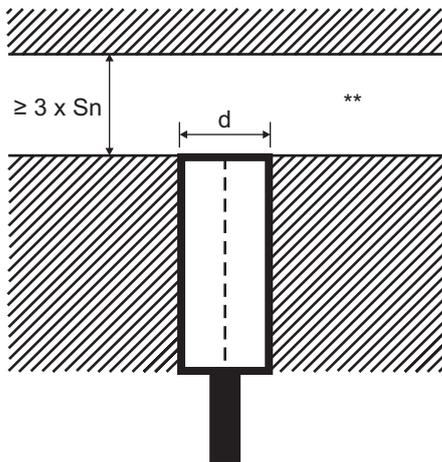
Lange Ausführung, bündiger Einbau, Steckversion
